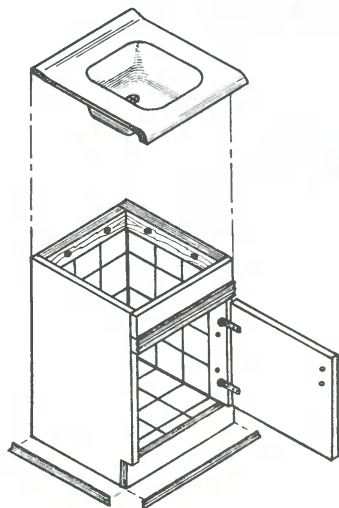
Общий вид мойки с бескорпусной тумбой.
